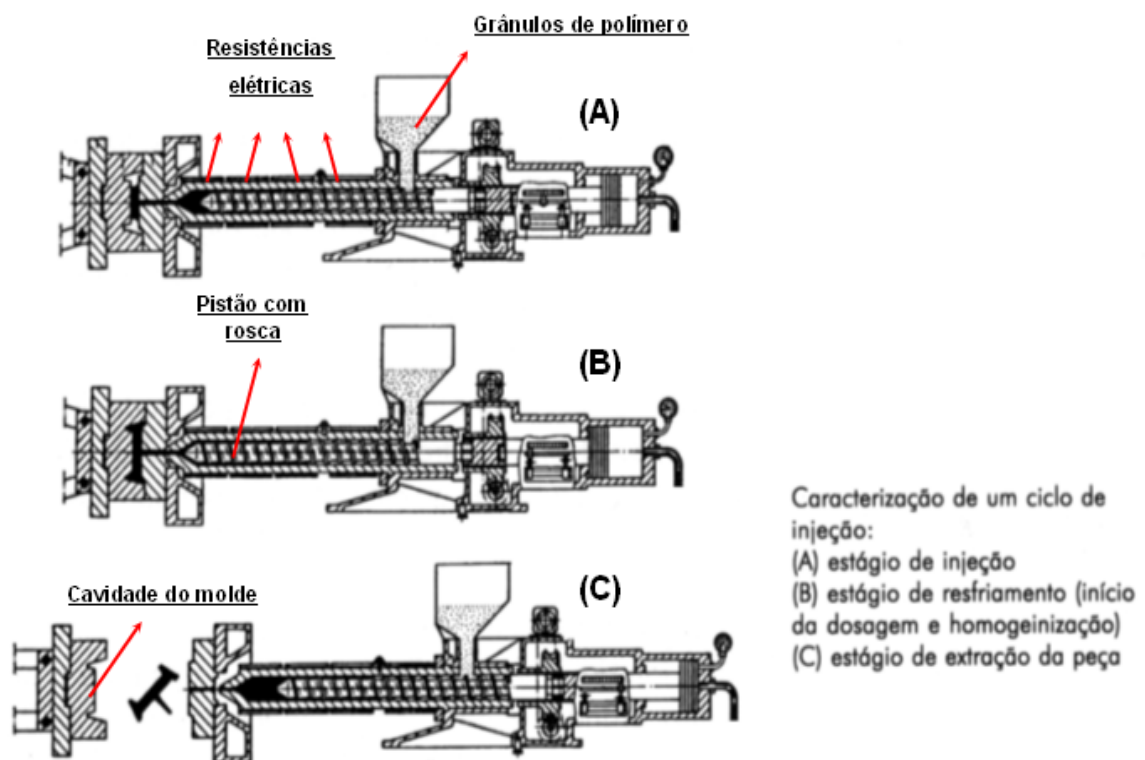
Máquina injetora e o ciclo do processo de moldagem por injeção^[28]
